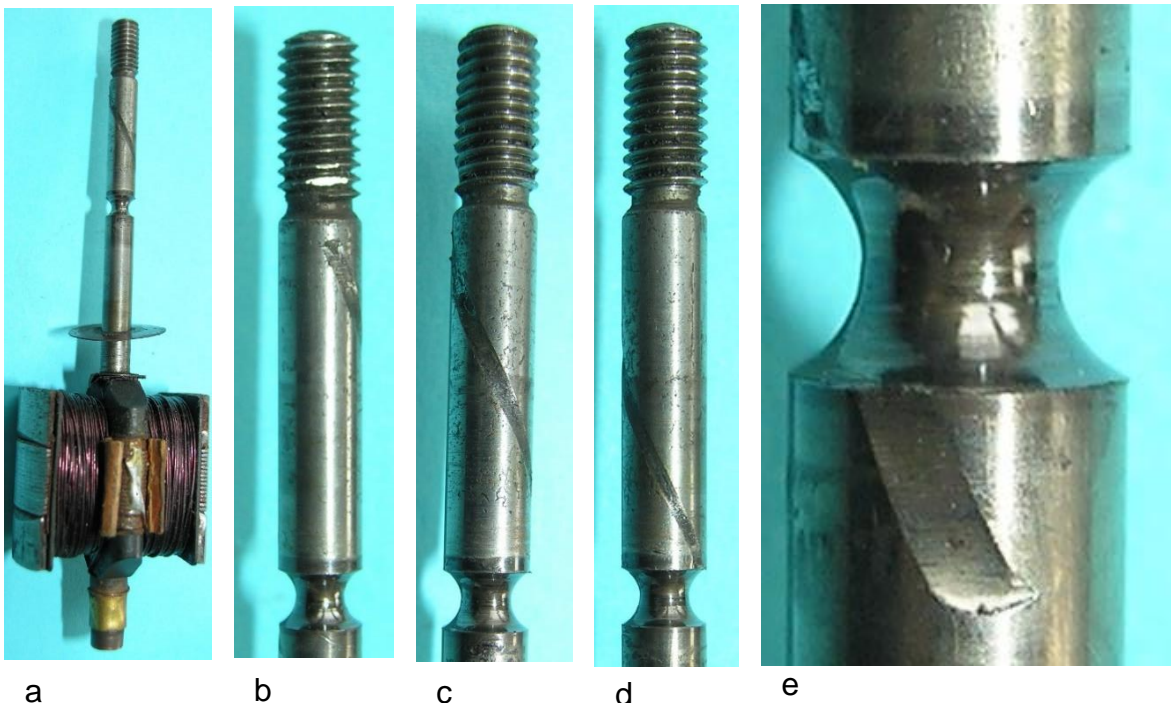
Welle mit spiralförmiger Nut für die Umlaufschmierung
